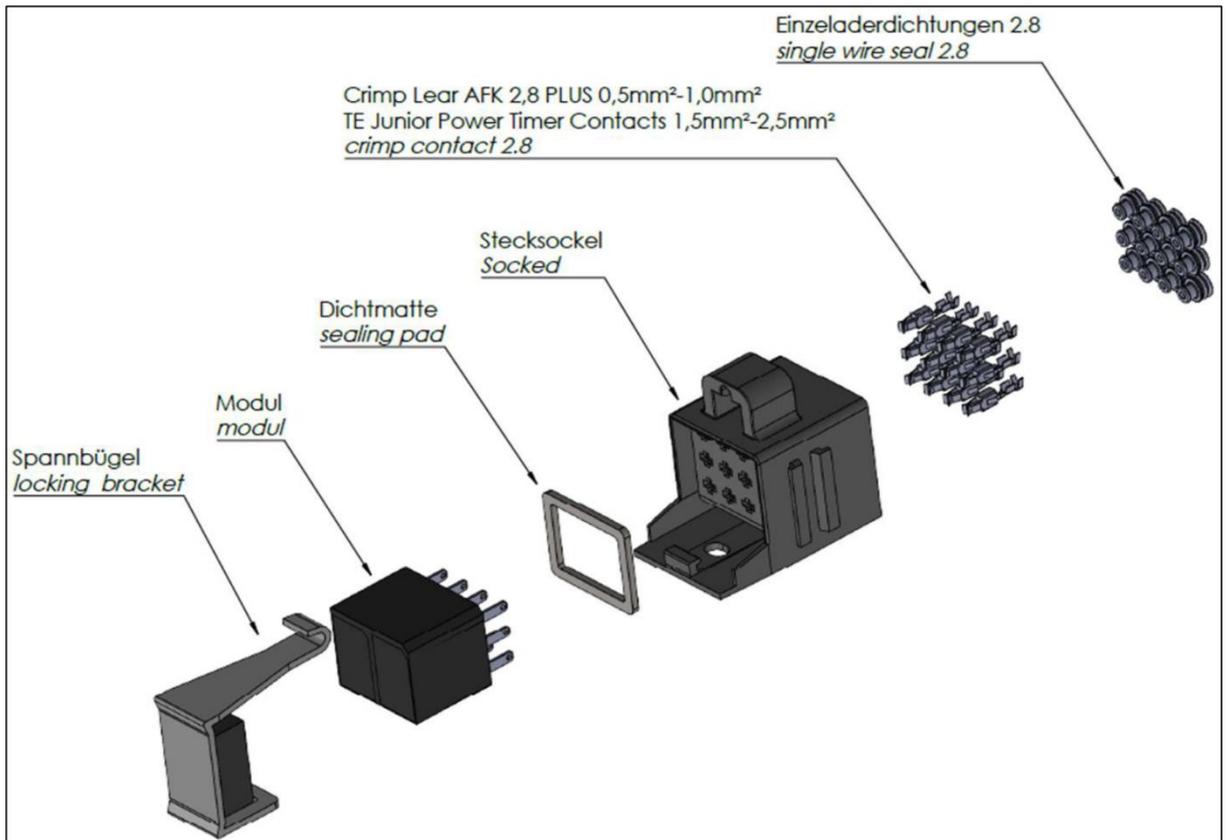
Explosionszeichnung wasserdichter Stecksocket (für Modul 1.017.055).
